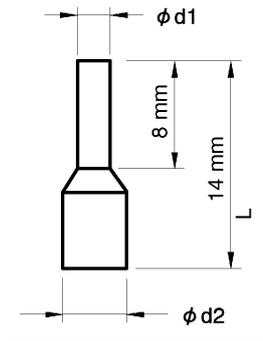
Dimensions de la borne sans soudure droite
